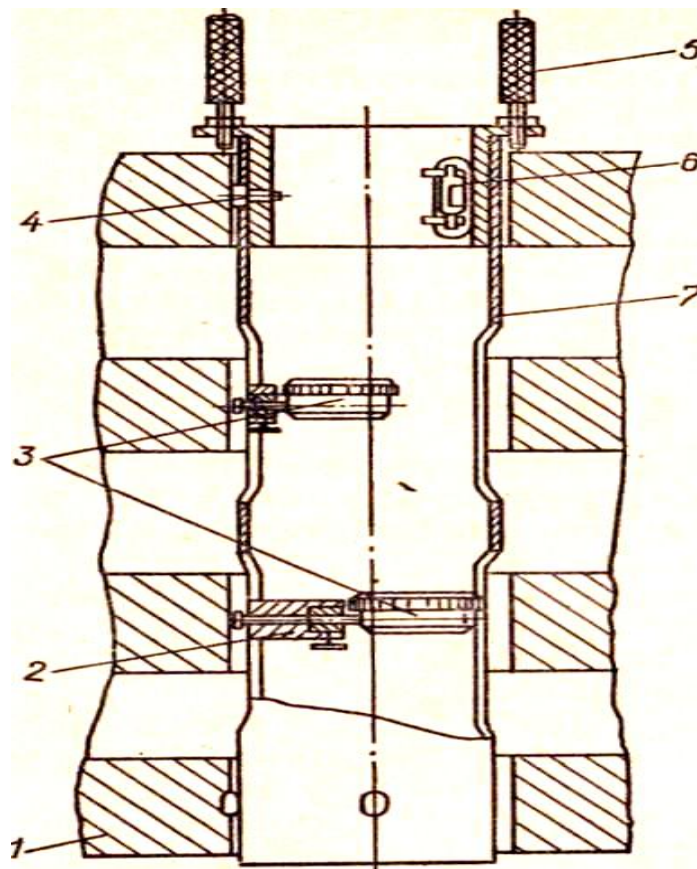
Пристрій для контролю взаємного зміщення опор блок-картра під колінчастий вал двигуна.
